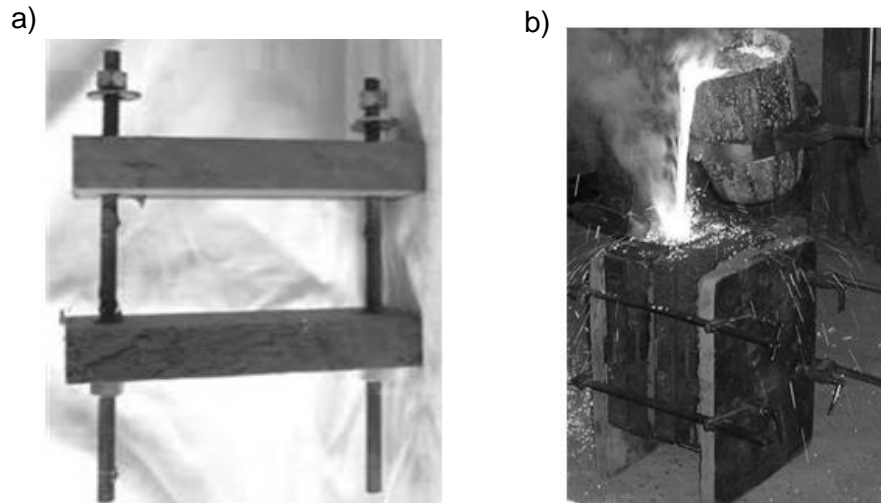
Tipos de prensa: embocaduras a) de planta y b) laterales.
